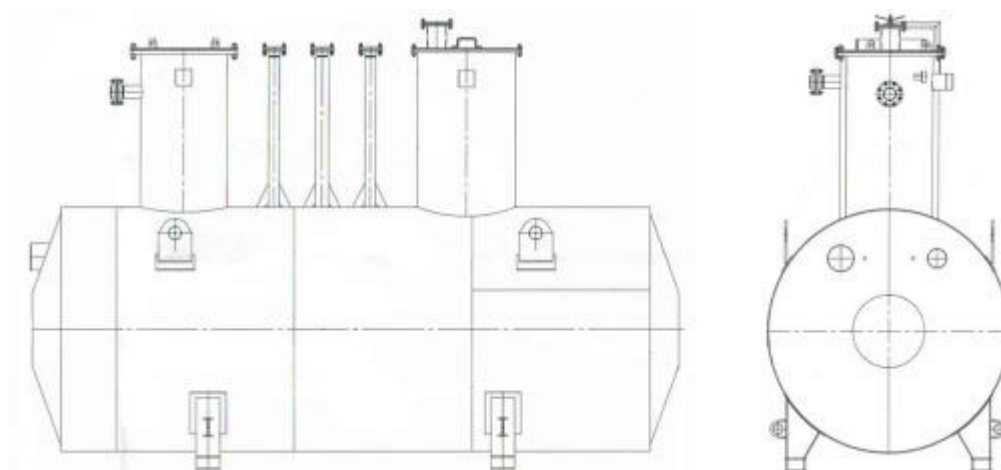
Эскиз общего вида резервуаров ЕП-16
